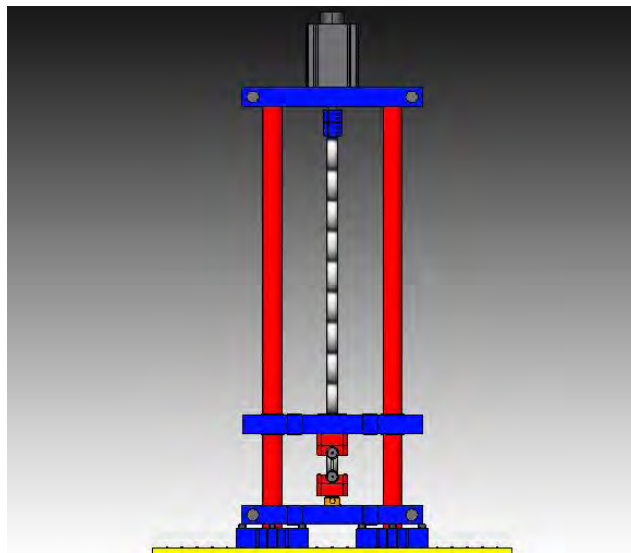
Ensamble general del Probador Mecánico. Vista frontal
